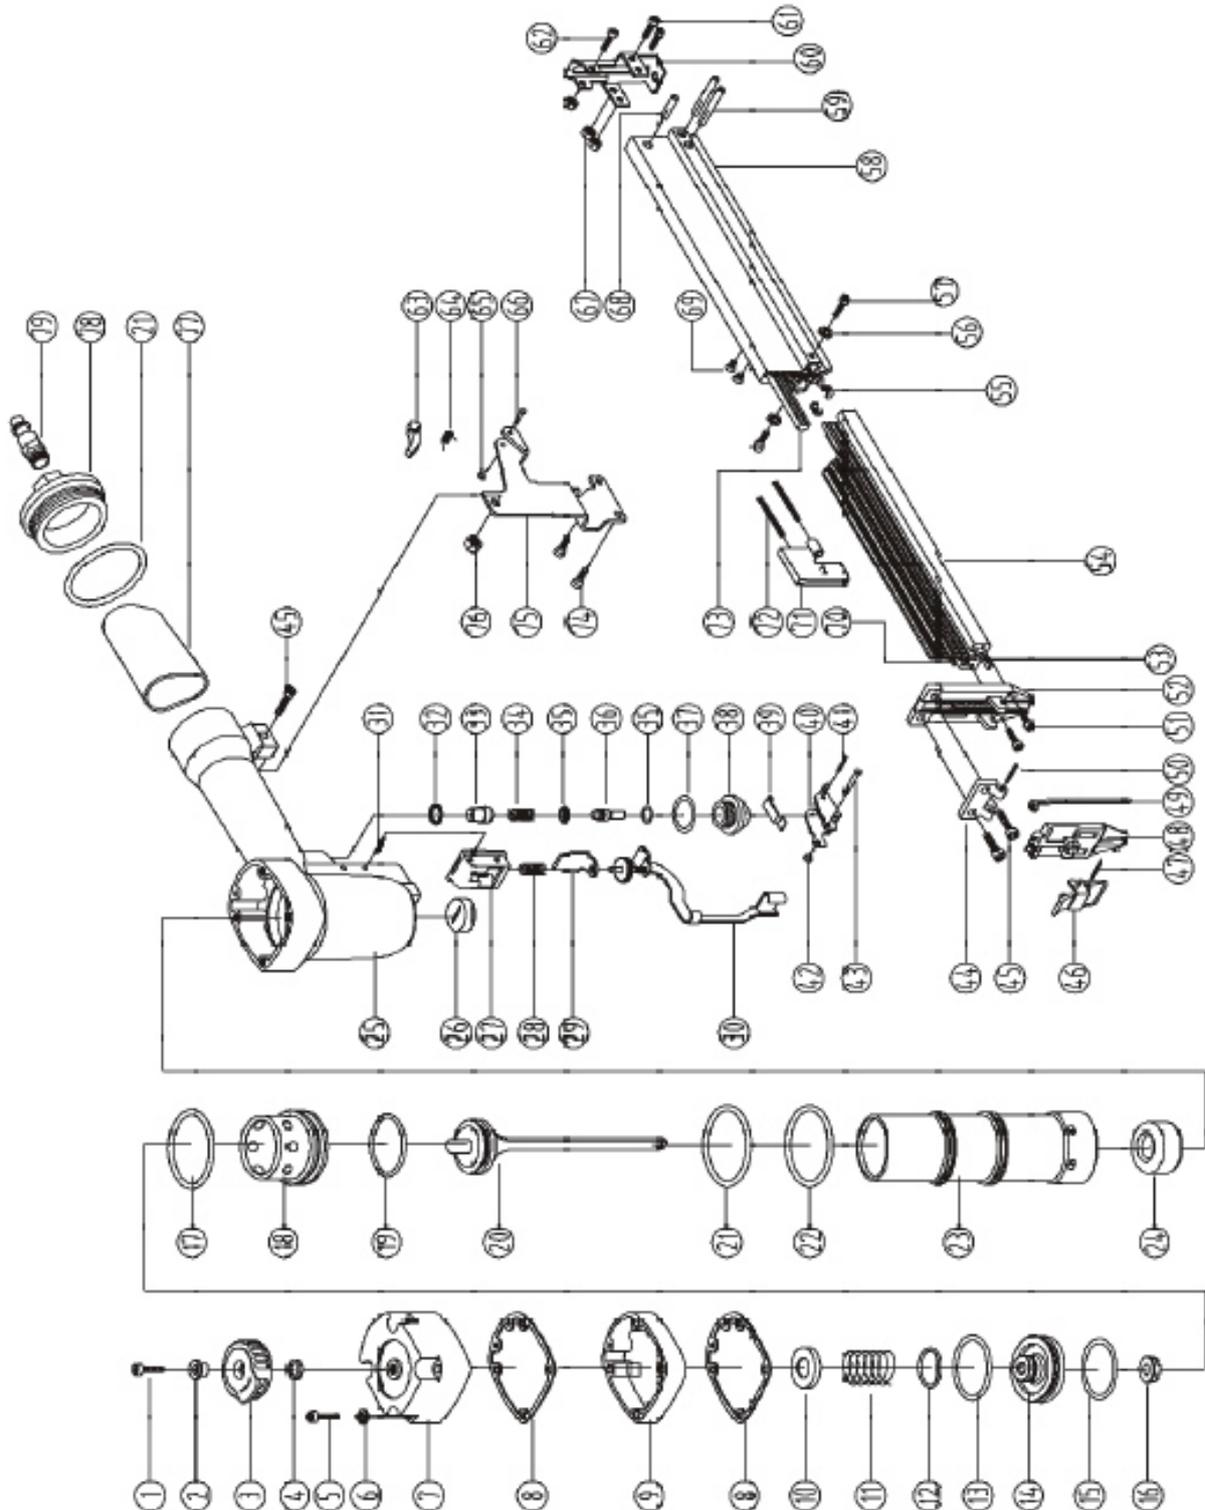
Ersatzteilzeichnung / Spare parts drawing
